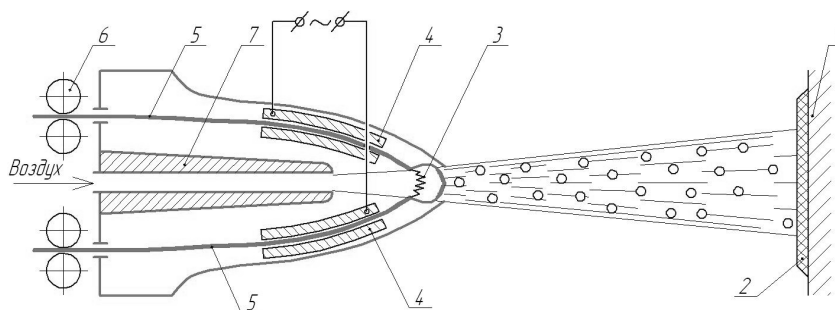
Схема электродугового напыления: 1 – восстанавливаемая деталь; 2 – покрытие; 3 –электрическая дуга; 4 – скользящий контакт; 5 – присадочная проволока; 6 – механизм подачи проволоки; 7 – сопло для подачи воздуха
